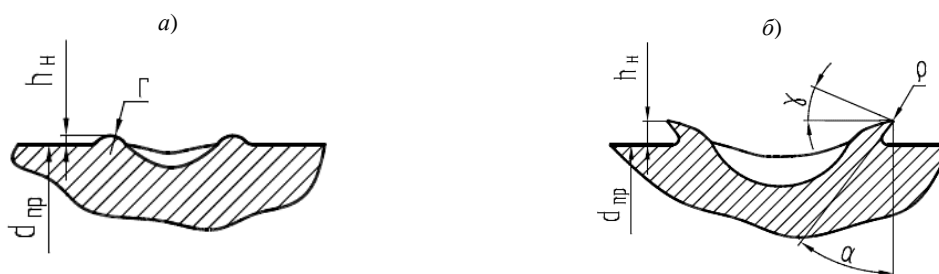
Схема наплывов металла, формируемых на поверхности проволоочного инструмента в процессе ЭКО
